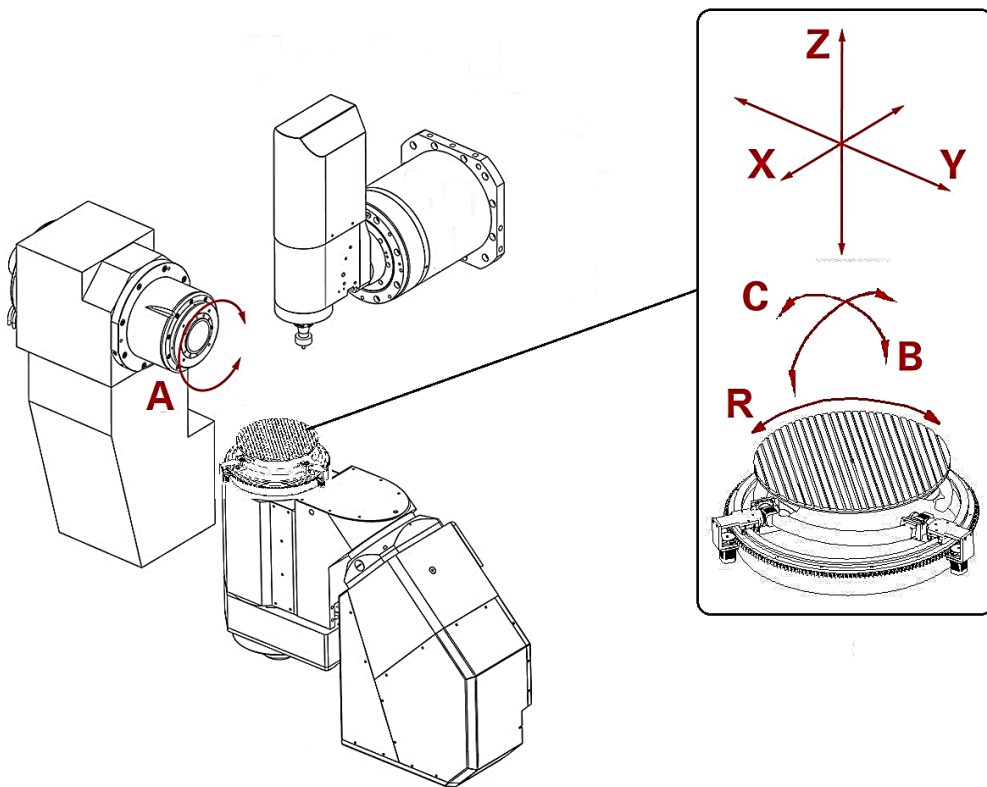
Обрабатывающий центр на основе предлагаемого механизма параллельной структуры для работы с малогабаритными деталями
